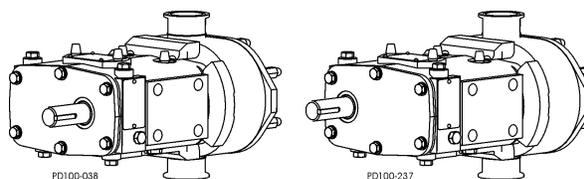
Montage latéral gauche et droit (vue depuis le couvercle de la pompe)
